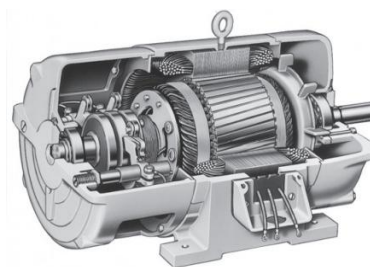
Motor de indução trifásico de rotor bobinado [9].
